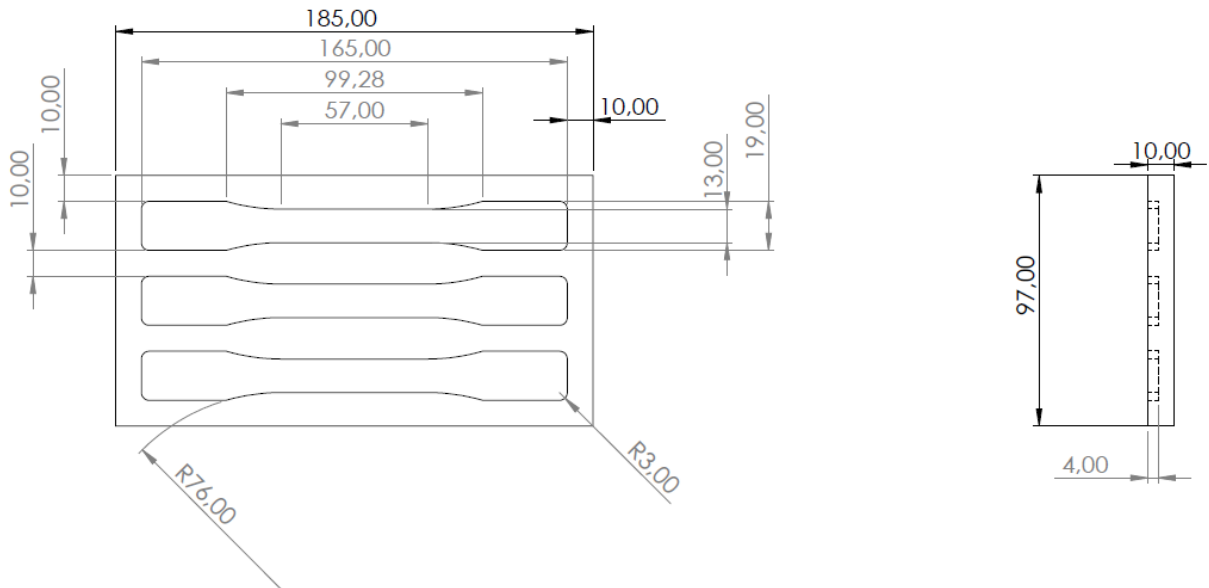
Molde para ensaio de tração segundo norma ASTM D638.14 [29] com dimensões em mm.
